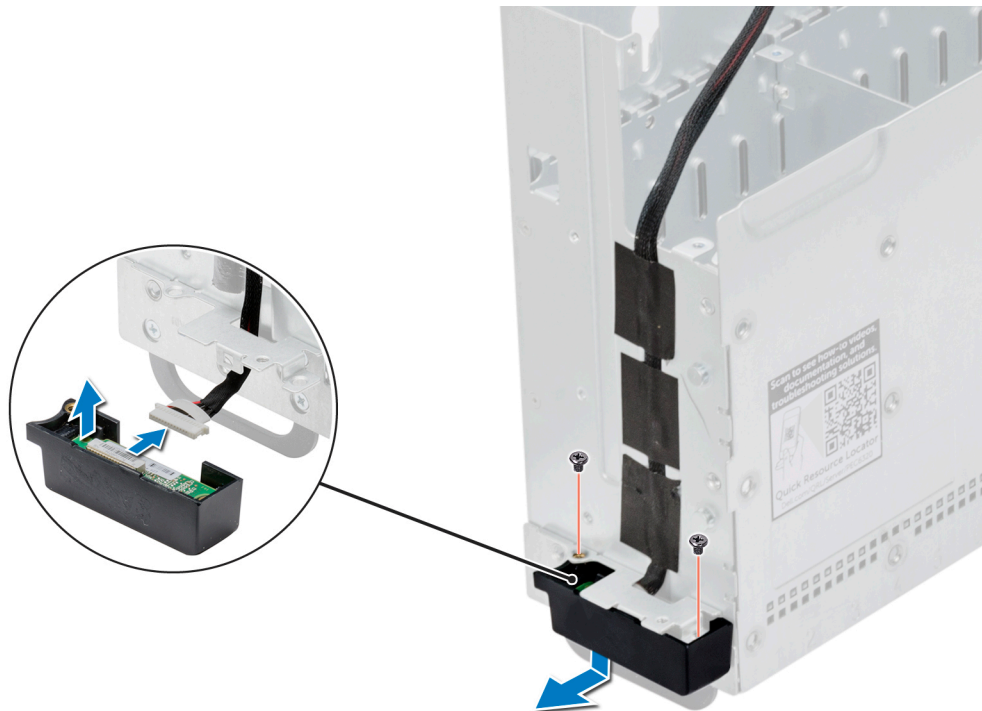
Extracción del ensamblaje del panel de control izquierdo
